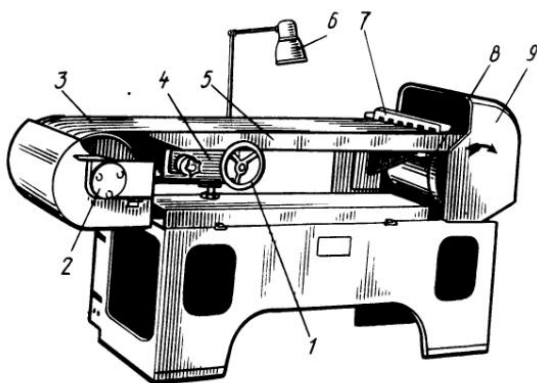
Ленточный шлифовальный станок с неподвижным столом:
